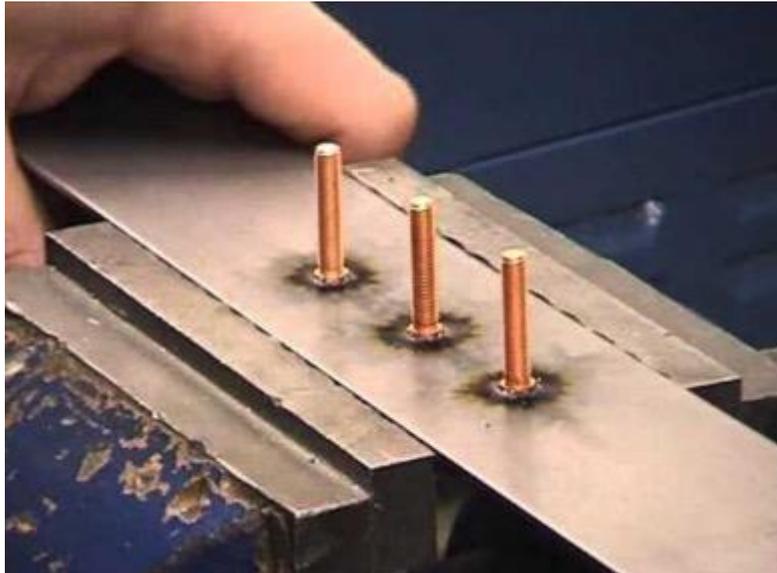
Soldadura realizada por descarga de condensadores. [3]
